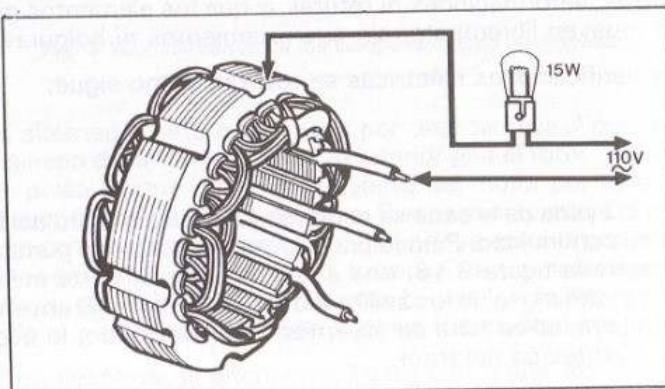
Conexión de la serie para la comprobación de aislamiento del bobinado del estator.
